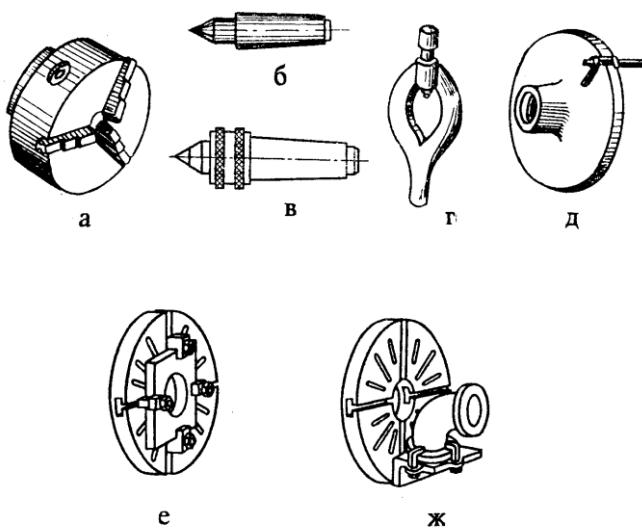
Приспособления для закрепления заготовок на токарных станках: а – трехкулачковый самоцентрирующий патрон; б – неподвижный упорный центр; в – врачающийся центр; г – хомутик; д – поводковый патрон; е – планшайба; ж – планшайба с угольником
